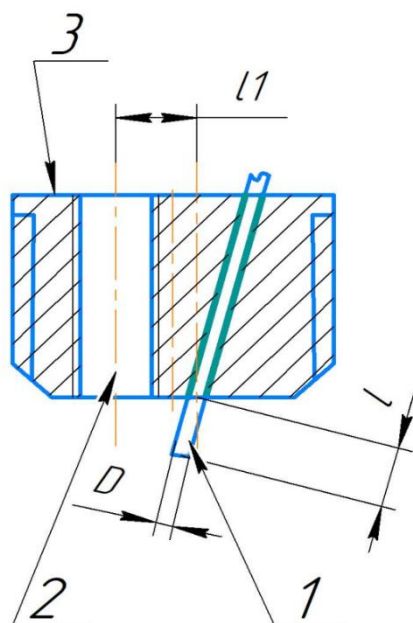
Схема ИД, изготовленного в одном корпусе со свечой зажигания 1- зонд (ИД); 2 – отверстие для установки свечи зажигания; 3 – корпус датчиков
